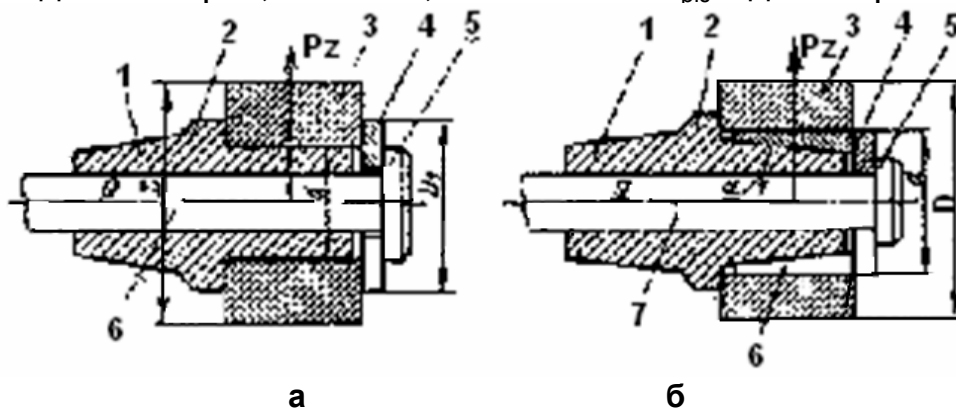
Конструкції оправок: а – гладка оправка; б – оправка з розрізною втулкою
